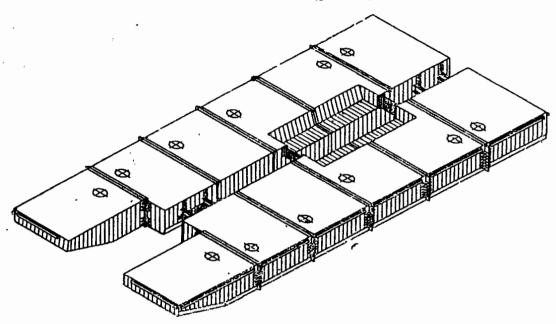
Общий вид корпуса земснаряда типа 12А-4.
